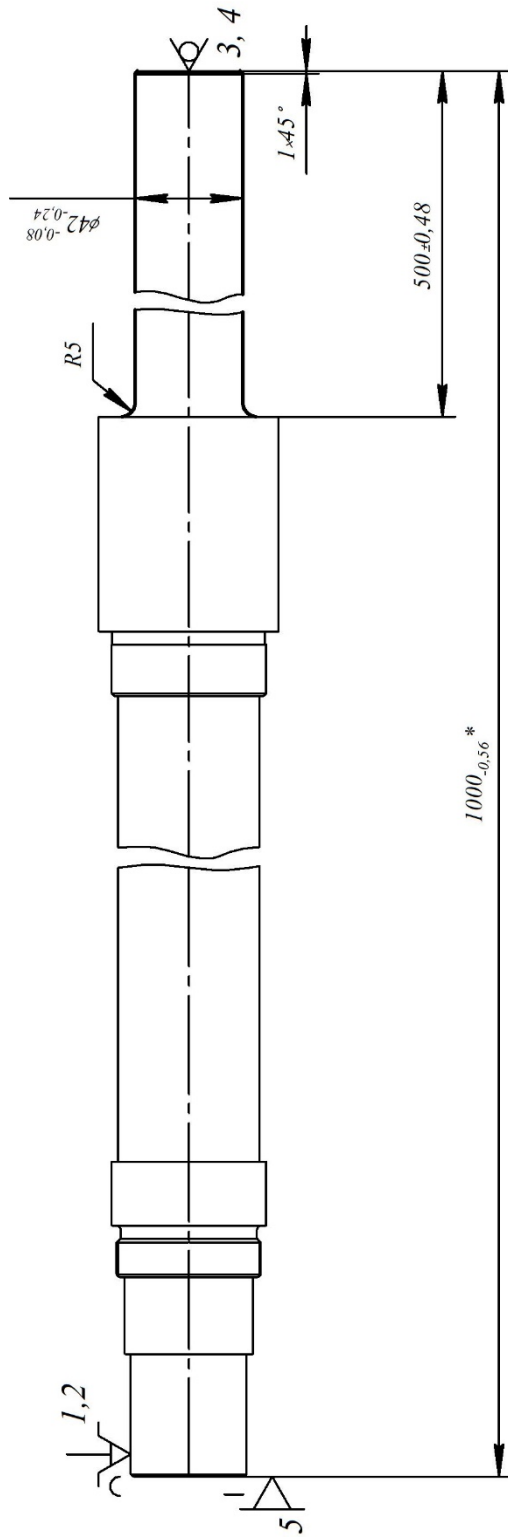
Альтернативна схема базування заготовки на операції токарній 025, установ Б
